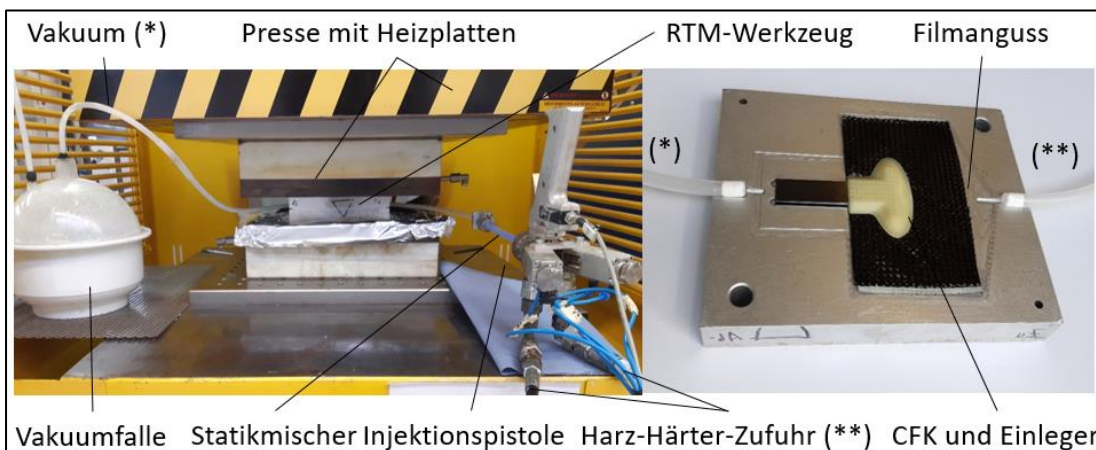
Aufbau des Injektionsprozesses in einer Presse, RTM-Werkzeug mit CFK und Einleger
